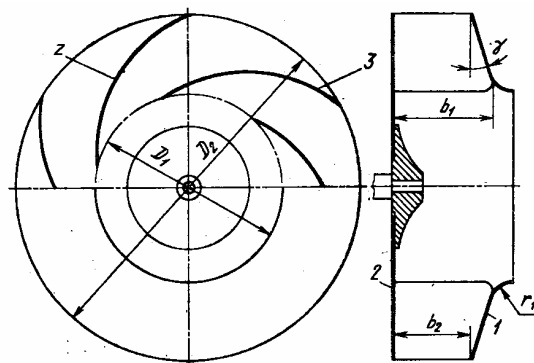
, б. Рабочее колесо: 1 — передний диск; 2 — задний диск;
